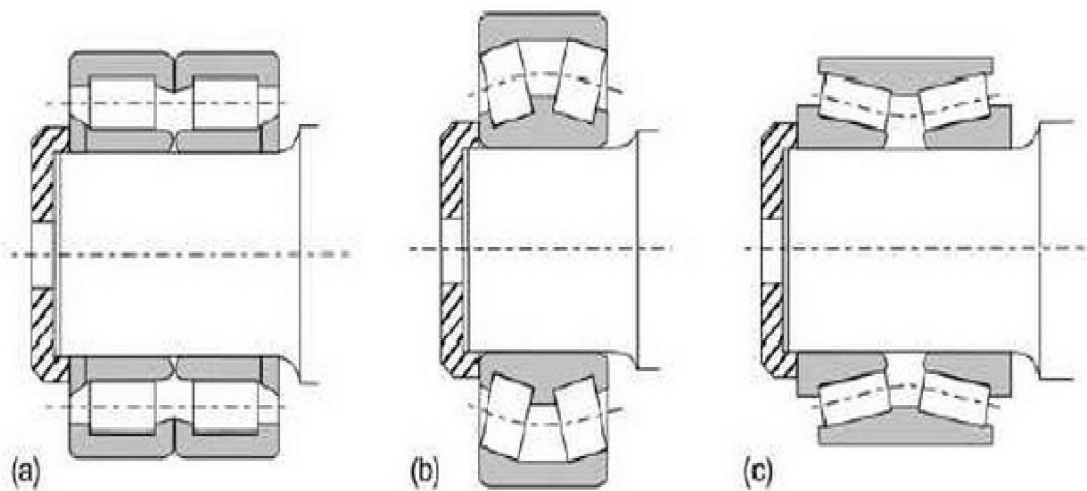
Diseños de rodamientos de rodillos: (a) cilindro de dos hileras (b) autoalineado de una hilera (c) cónico de dos hileras [5]
